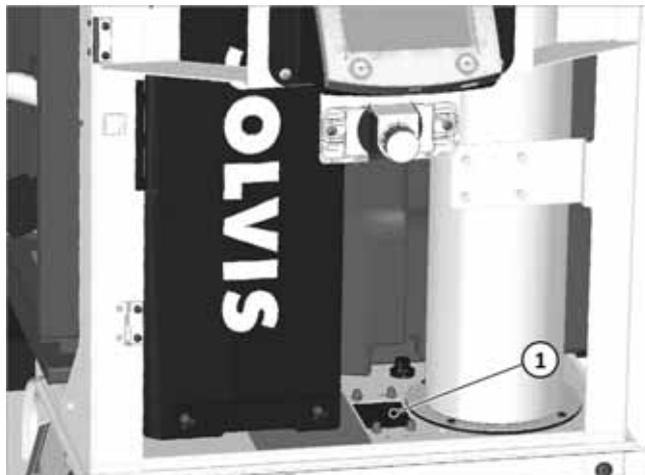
Passaggio cavo di collegamento attraverso la piastra di base (1)
